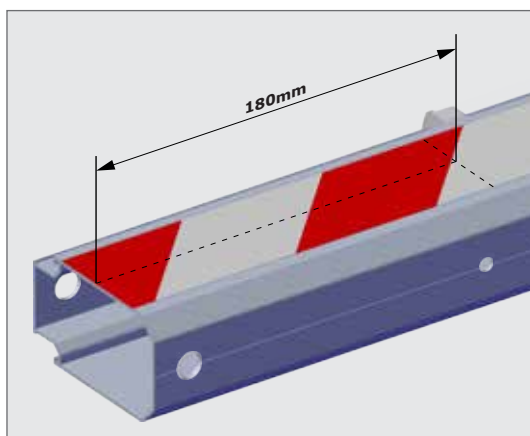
CÔTÉ DE LA BARRIÈRE LEVANTE
